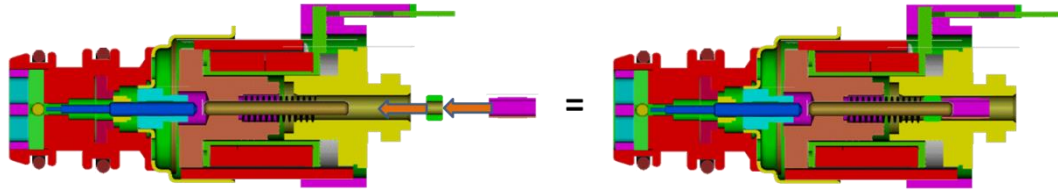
Ensamble de rodamiento y casquillo de ajuste.
